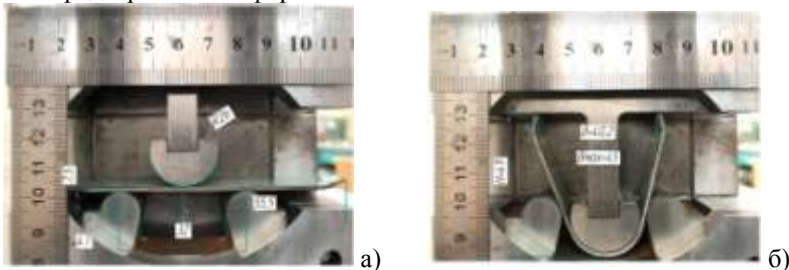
Предварительная формовка: а) исходное положение т.з. перед процессом предварительной формовки; б) U-образная заготовка под нагрузкой в прессе
